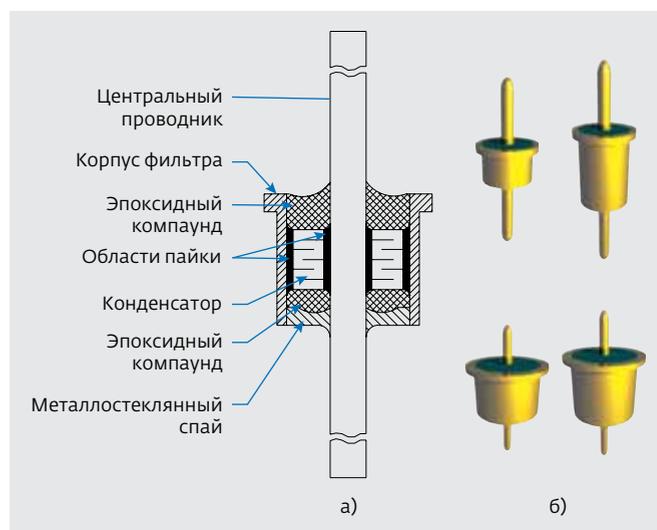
Конструкция (а) и внешний вид (б) миниатюрных герметичных безрезьбовых фильтров
